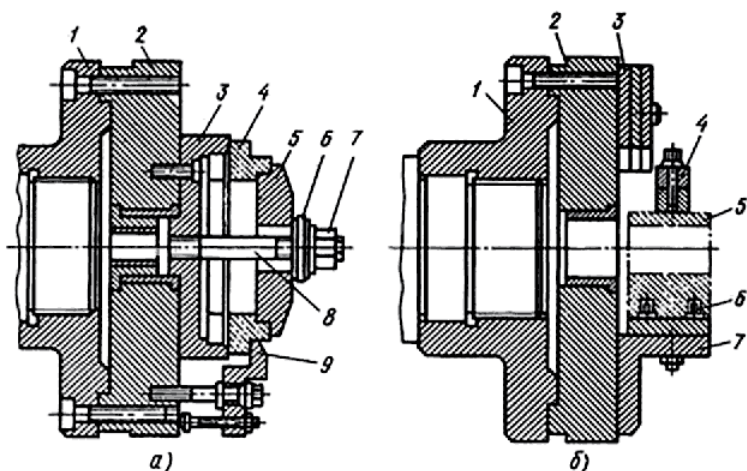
Примеры закрепления заготовки на планшайбе
